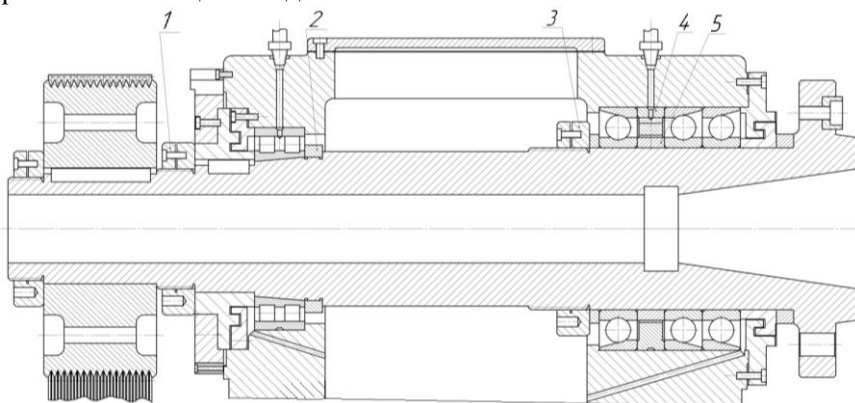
Шпиндельный узел автономной шпиндельной бабки с ременным приводом токарного станка с шариковыми радиально-упорными подшипниками триплекс тандем О-образный в передней опоре и роликовым радиальным цилиндрическим – в задней
